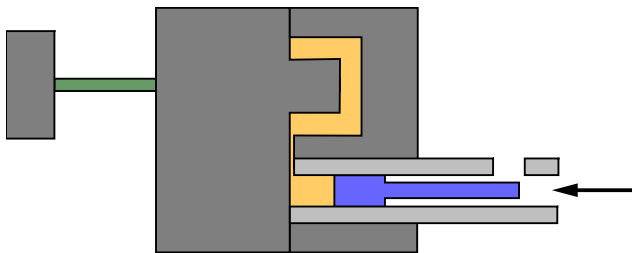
rfZ) Der Kolben drückt das flüssige Metall in das Werkzeug
